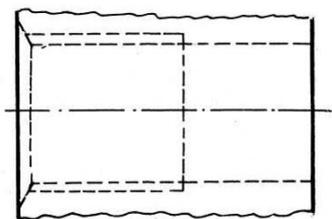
Резьба, показываемая как невидимая в цилиндрическом отверстии
